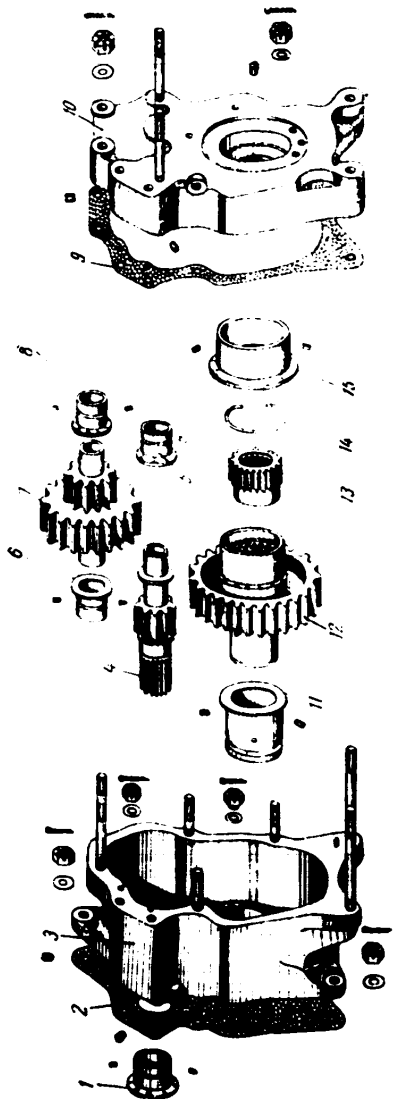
Задняя крышка картера, собранная с зубчатыми колесами привода.
